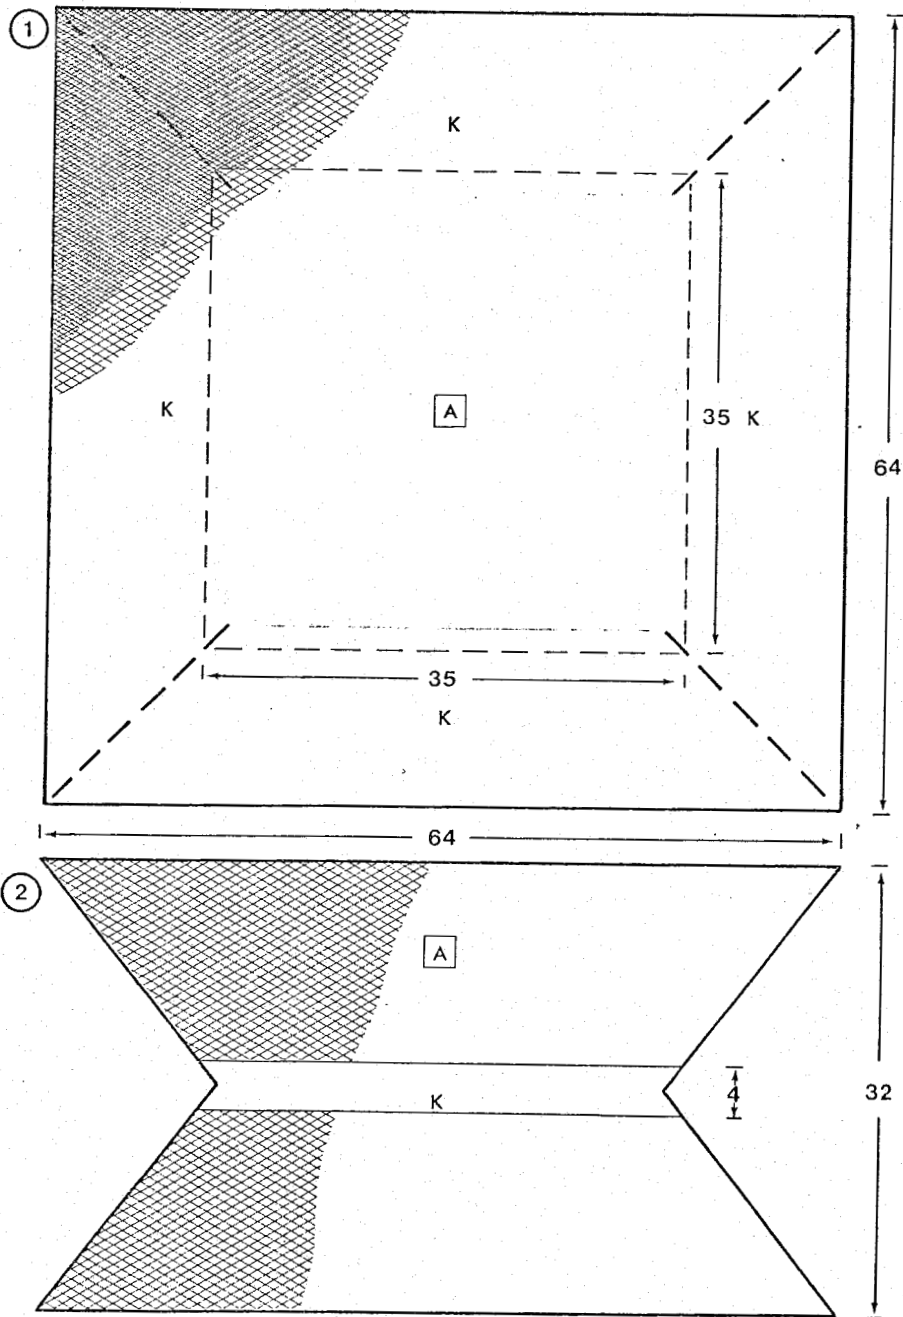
Teinetype 15. Kvadratisk, prismeformet konstruksjon med spalteformet "midjekalv". Alle mål i cm.
